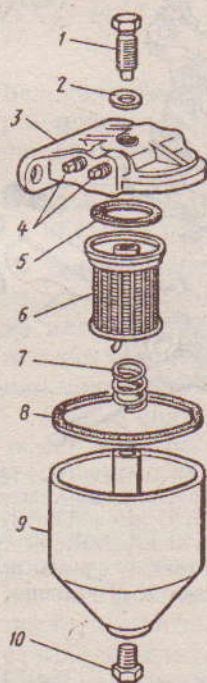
Отстойник бензиновый: 1 - болт М10; 2 - шайба 11; 3 - крышка; 4 - пробка; 5 - прокладка; 6 - фильтрующий элемент; 7 - пружина; 8 - прокладка; 9 - корпус; 10 - пробка сливная
